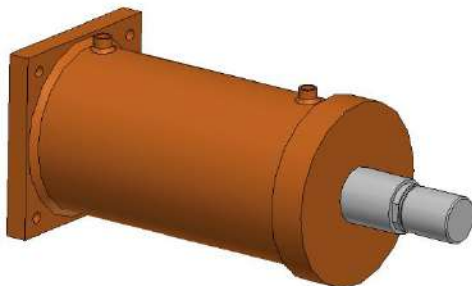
Diseño 3D del cilindro seleccionado. Ver plano “CilindroCHA1” adjunto en el “Anexo 1: PLANOS”
